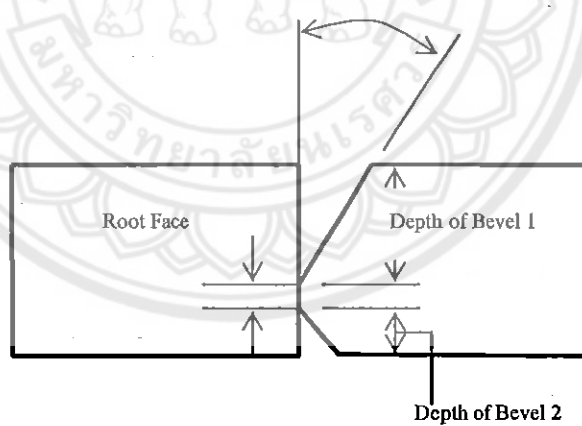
แสดง Single Bevel Single Side Weld [2]
